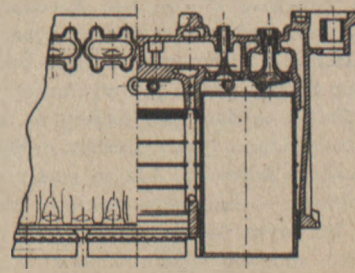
Oddzielny cylinder chłodzony cieczą.
